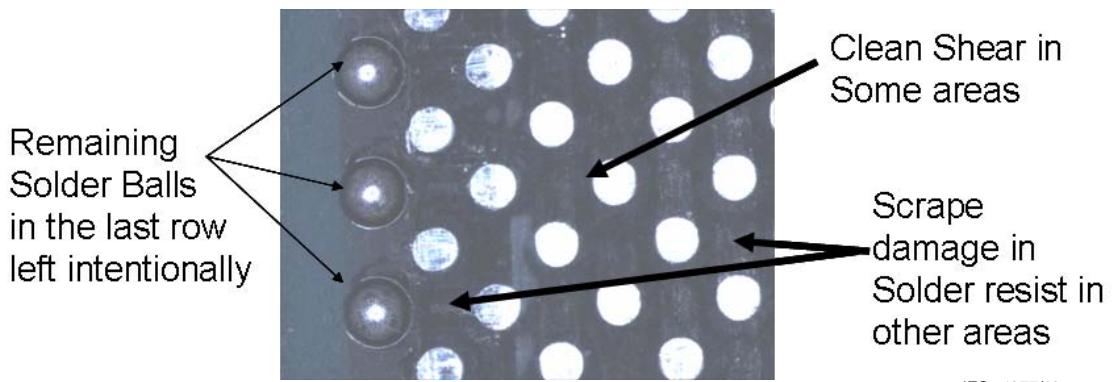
Matériau de bille de soudure recueilli d'un BGA en utilisant une procédure de retrait manuel
